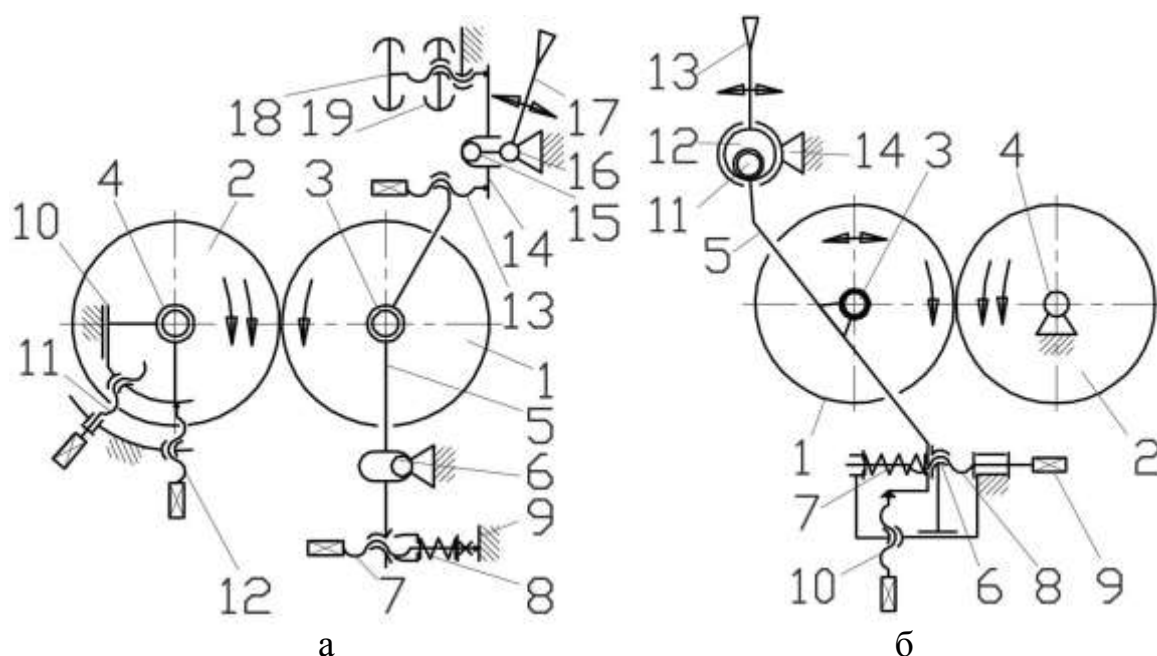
Схеми установчих механізмів вальцювих верстатів.
